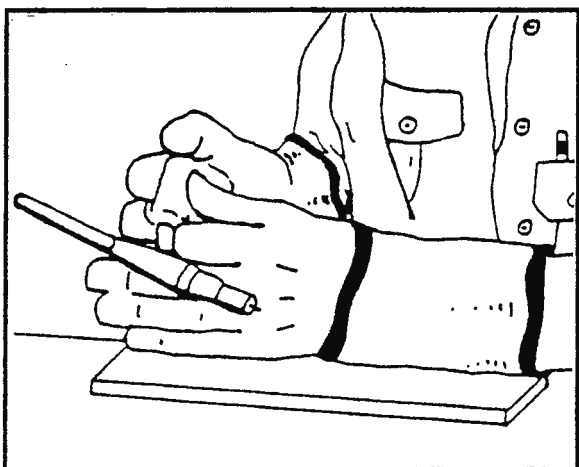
Posición de la Antorcha para iniciar el balanceo
